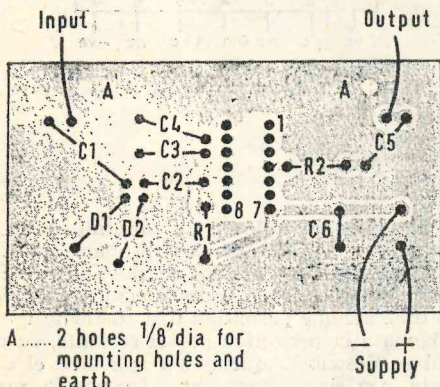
Panel del circuito impreso visto por el lado de cobre. (Tamaño real.)
